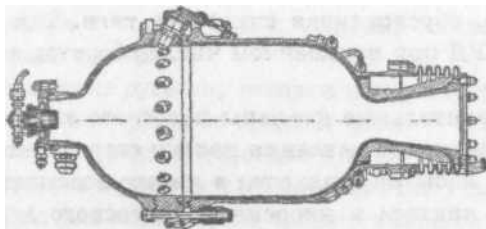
Камера ЖРД РД-2 В.П. Глушко [12]
